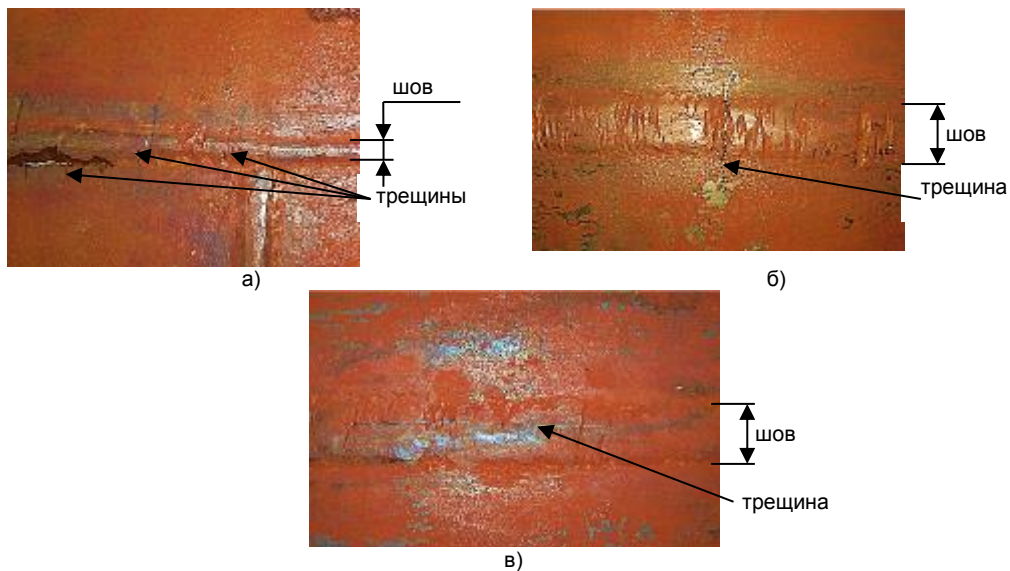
Трещины на образцах сварных соединений с продольным и пересекающимися сварными швами после испытаний на КРН.
